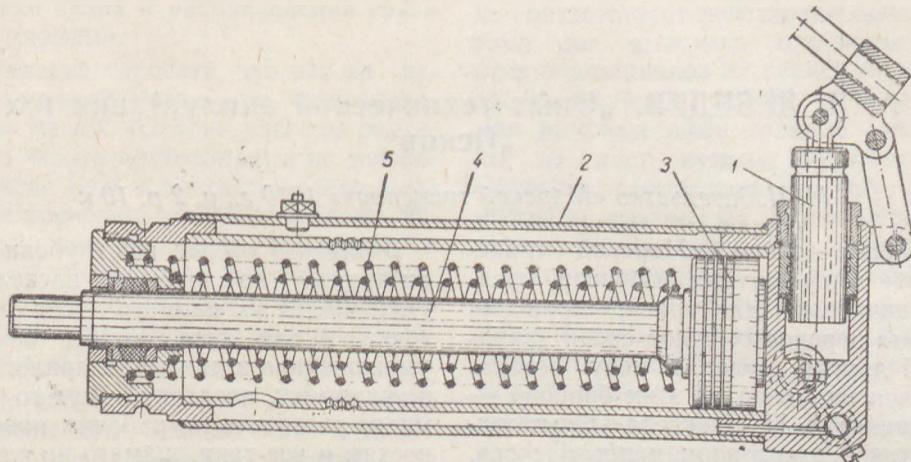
1 — насосная головка; 2 — двухстенный корпус; 3 — поршень; 4 — шток,
